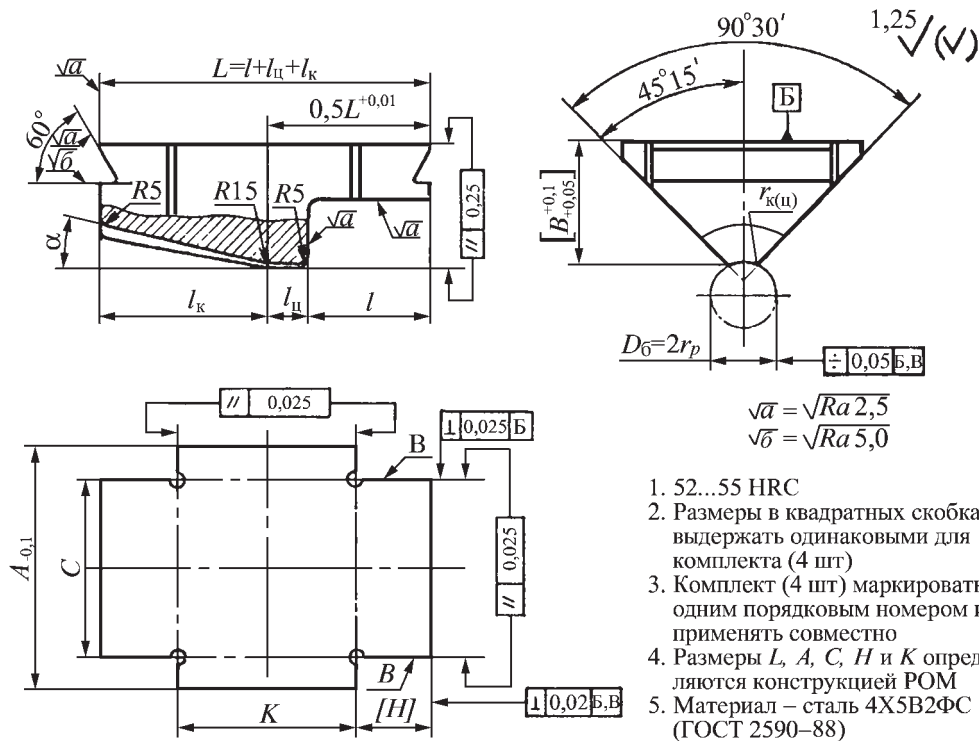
Чертеж бойка для профильного обжатия с одним заходным конусом α
